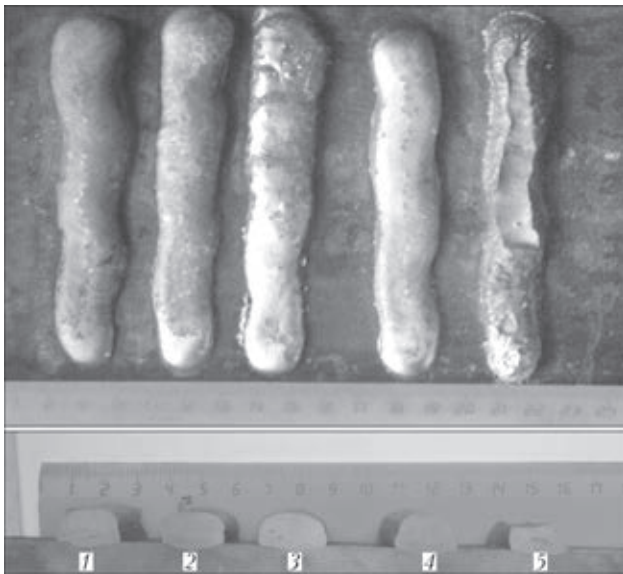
Внешний вид наплавки под различными флюсами: 1 — АН-60; 2 — АН-348А; 3 — АН-26С; 4 — АН-60СМ; 5 — UV 420 ТТ
